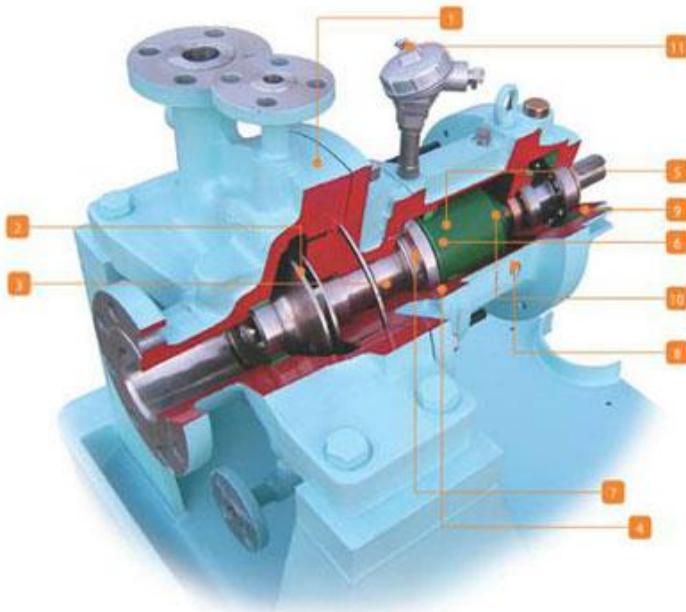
Основные детали нефтяного герметичного центробежного насоса: 1 – корпус насоса; 2 – рабочее колесо (закрытого типа); 3 – подшипник; 4 – уплотнительный стакан; 5 – внутренний магнит; 6 – внешний магнит; 7 – защитный кожух; 8 – вторичный кожух; 9 – несущая рама; 10 – масляное уплотнение; 11 – датчик температуры
